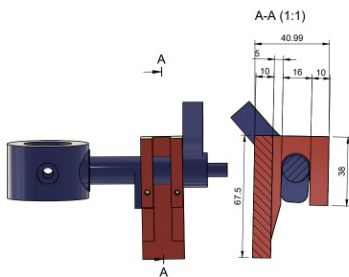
technische Zeichnung des Bauteil 6 der Baugruppe Schacht
